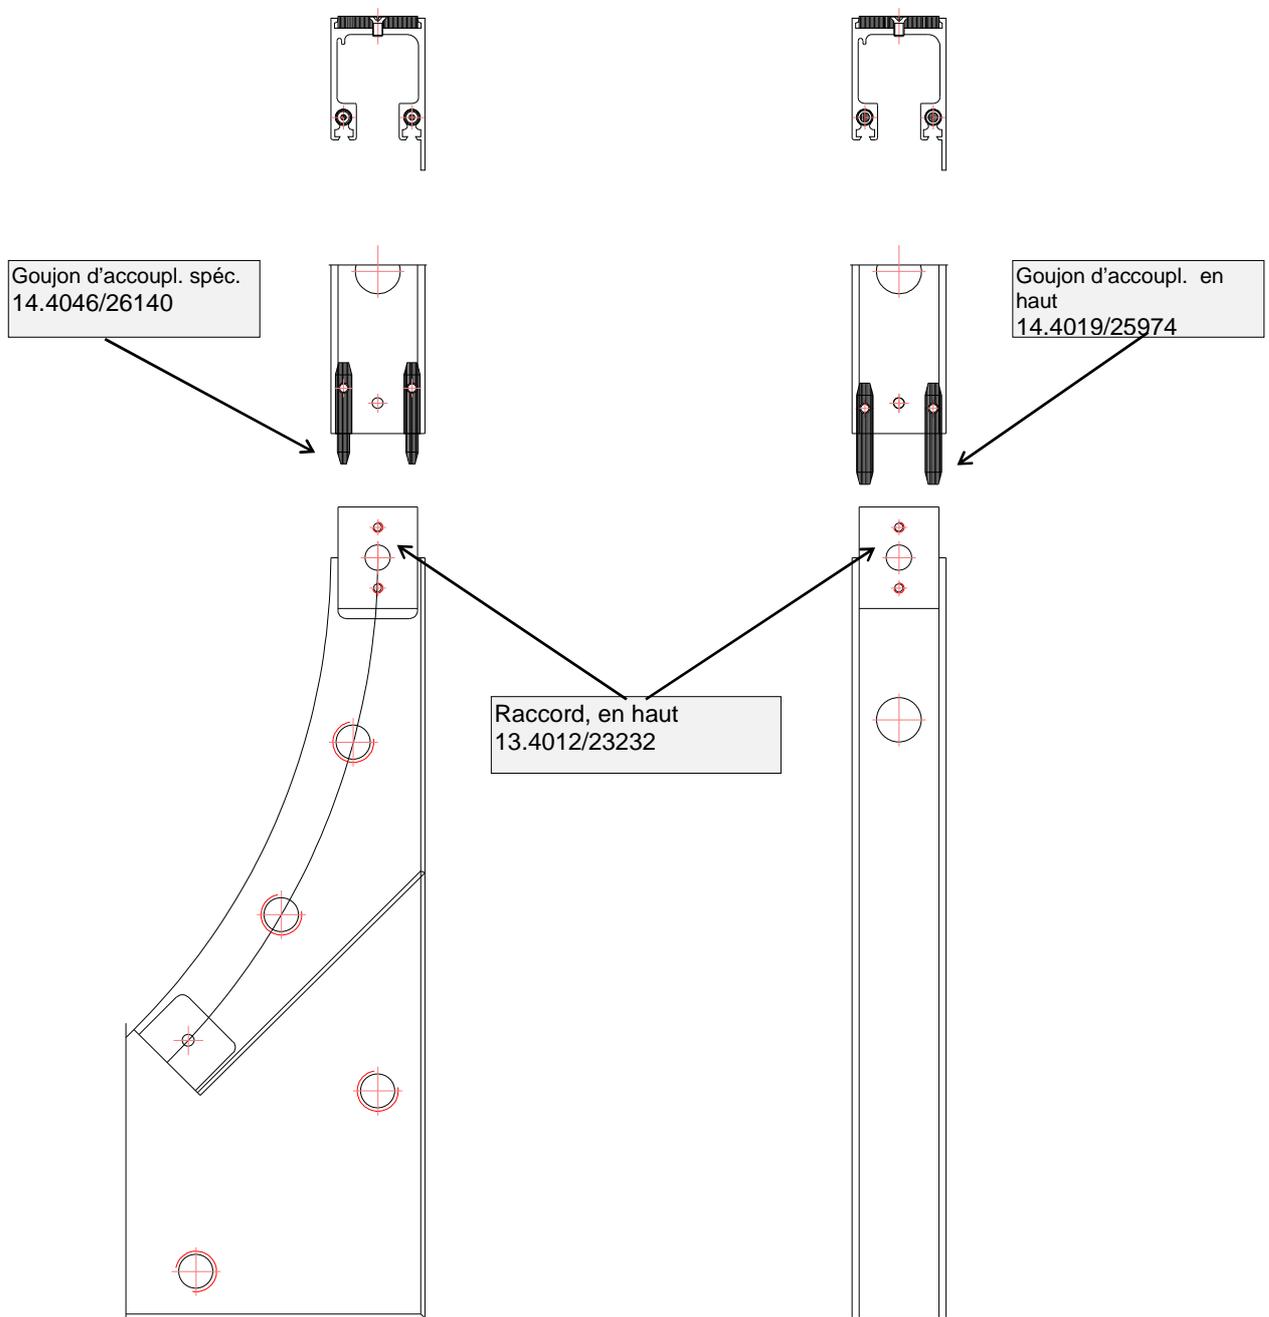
Vue Joint Arc plein-cintre en haut 90°+135°
